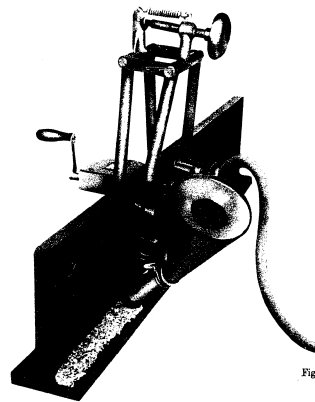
Специализированный держатель ДПП-16 для приварки фланцев к трубам
